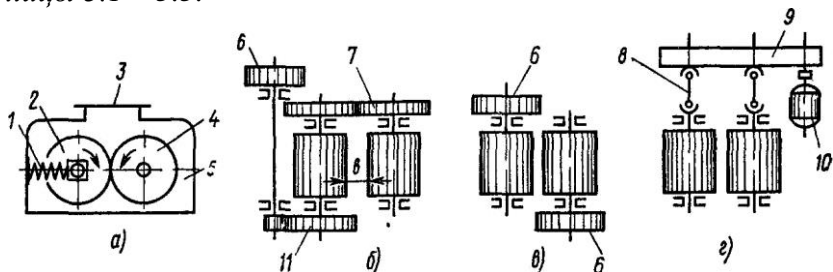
Схемы двухвалковой дробилки (а) и привода валков (б - г):
